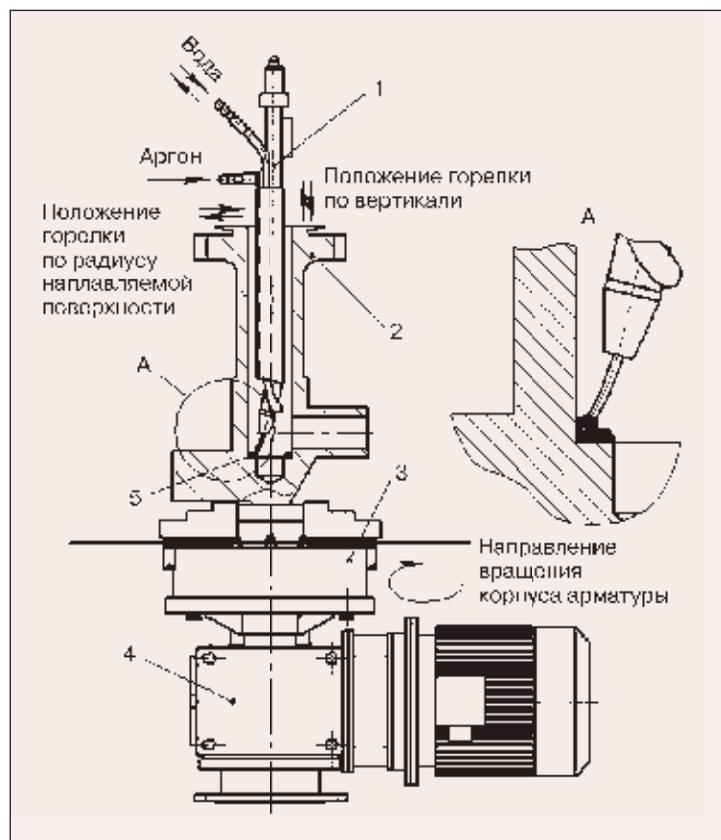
Схема наплавки корпуса арматуры: 1 — мундштук; 2 — корпус арматуры; 3 — зажимное устройство; 4 — вращатель; 5 — наплавляемая поверхность
